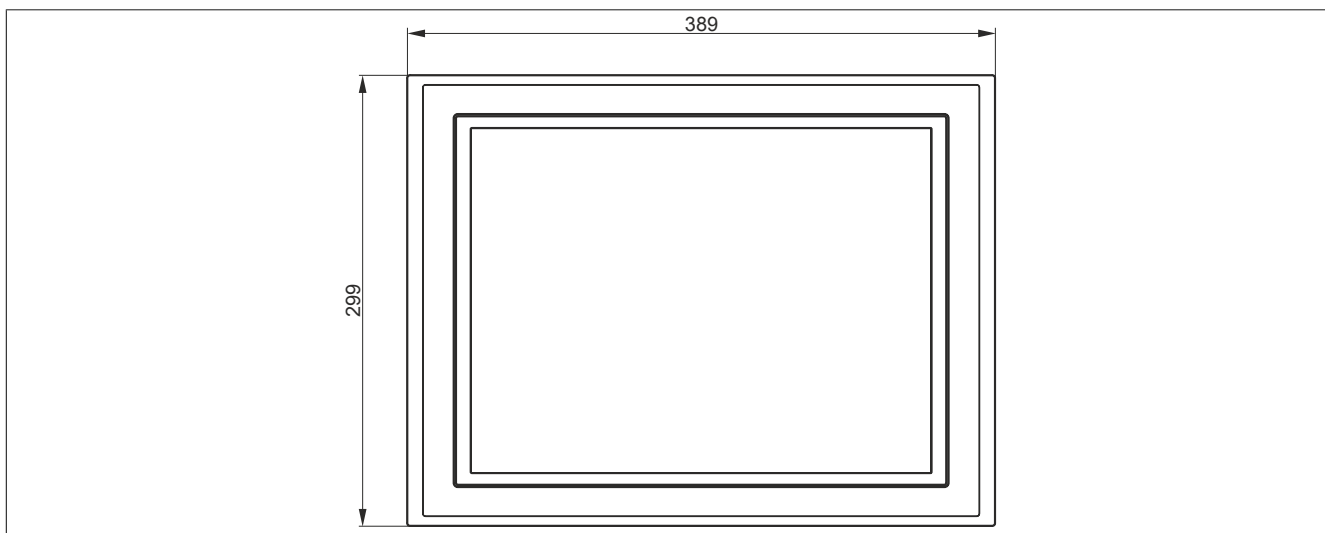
5AP5120.1505-000 - Abmessungen
